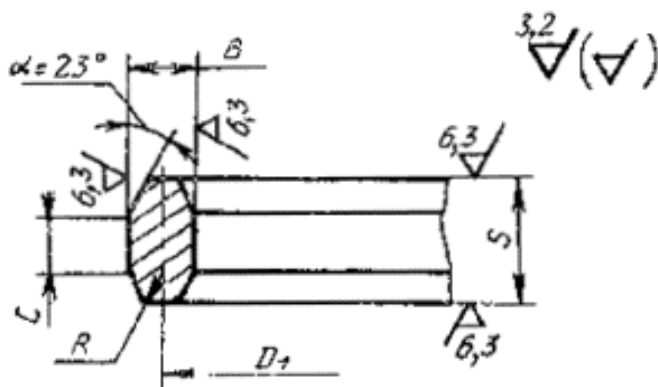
Конструкция прокладки восьмиугольного сечения.
